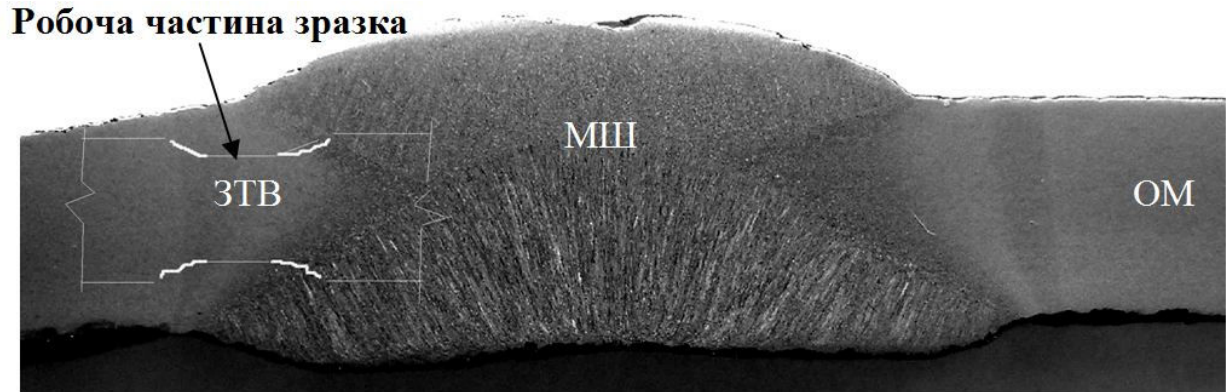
Фрагмент зварного з'єднання. Схема розташування робочої частини вкороченого циліндричного зразка в ЗТВ зварного з'єднання
